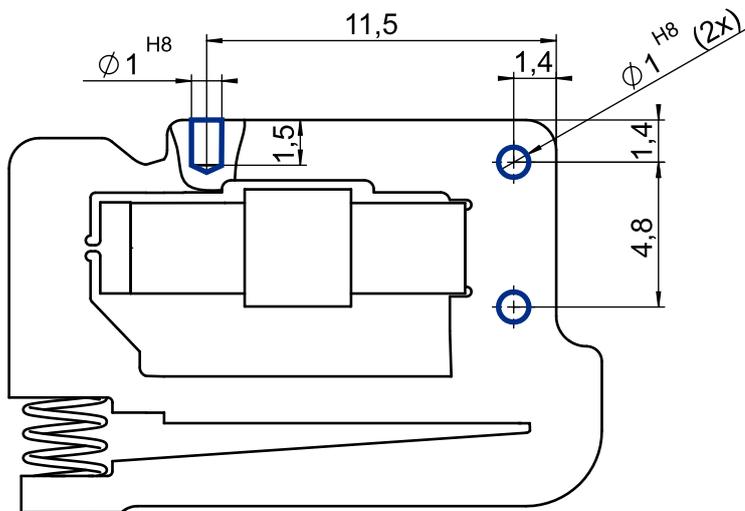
Montagebohrungen im Grundkörper des P-604.300
